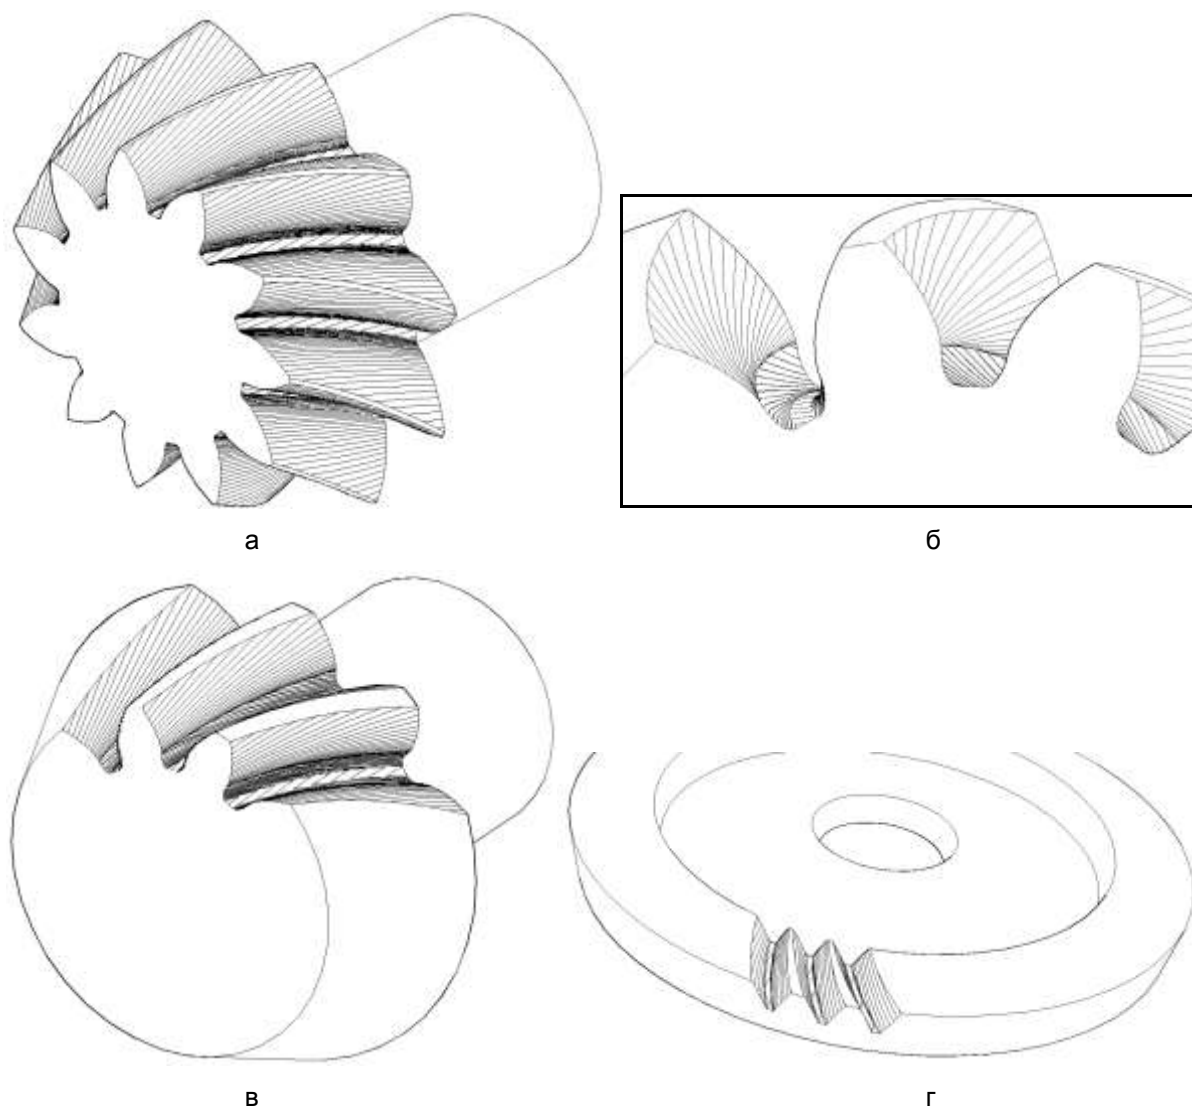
Различные формы зубьев гипоидной шестерни и колеса, полученные методом виртуального нарезания: а – заострение зуба по вершине; б – подрез зуба у его ножки; в – увеличенная ширина вершинной ленточки зуба; г – сужение ленточки зуба колеса со стороны «малого модуля»
